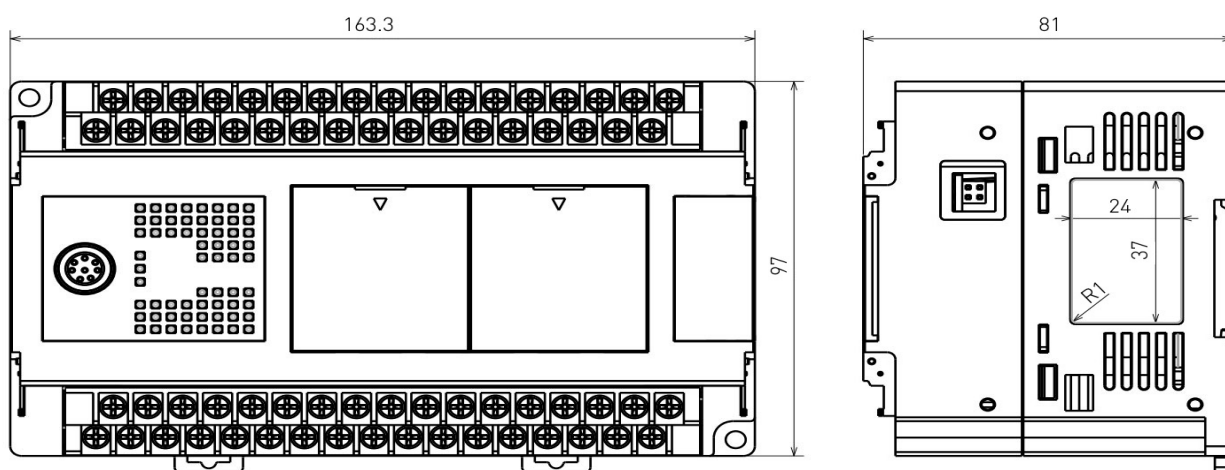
Габаритный чертеж PLC контроллера FAS-50MT-AC.
